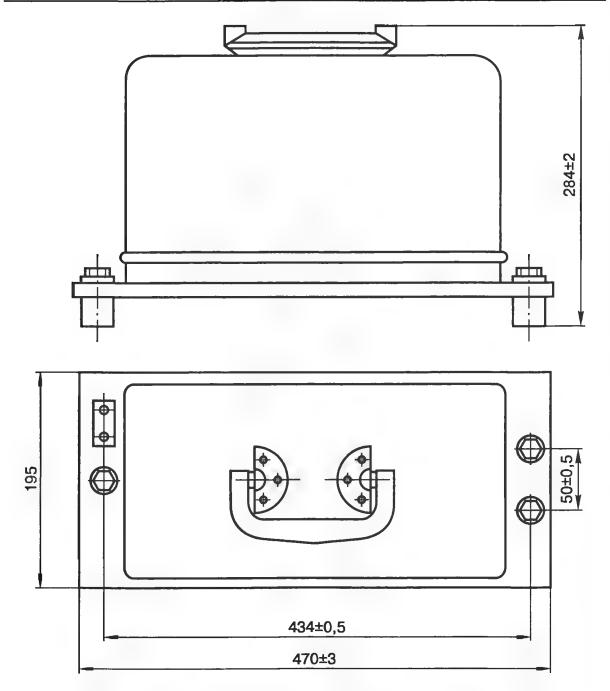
Общий вид дешифраторов ДКСВ-1-Д и ДКСВ-1-ДБ
